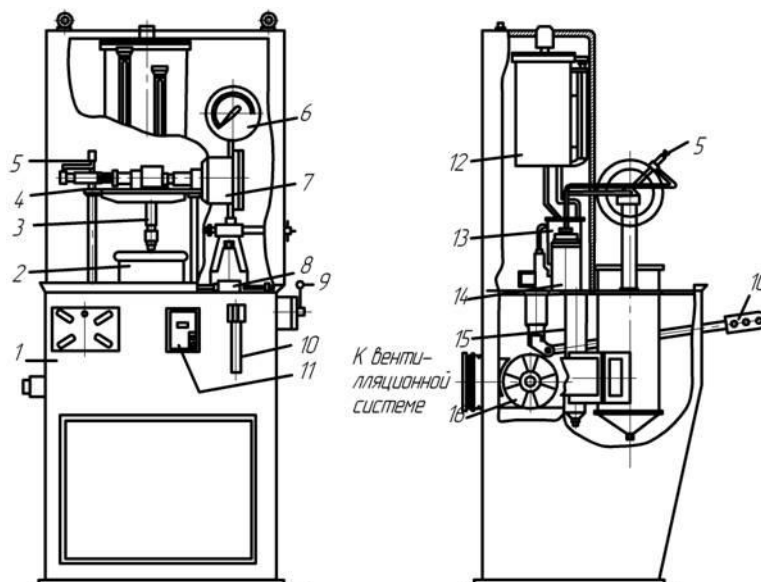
Стенд А106 для проверки работы форсунок ДВС:
